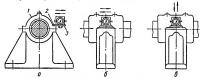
Схемы установки виброметра на подшипнике: 1 — подшипник; 2 — крепежная пластинка; 3 — вяброметр.
